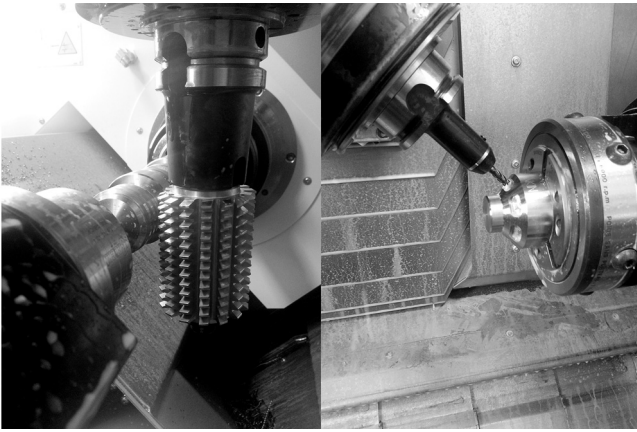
Токарно-фрезерный центр DMG CTX beta 1250 TC 4A
